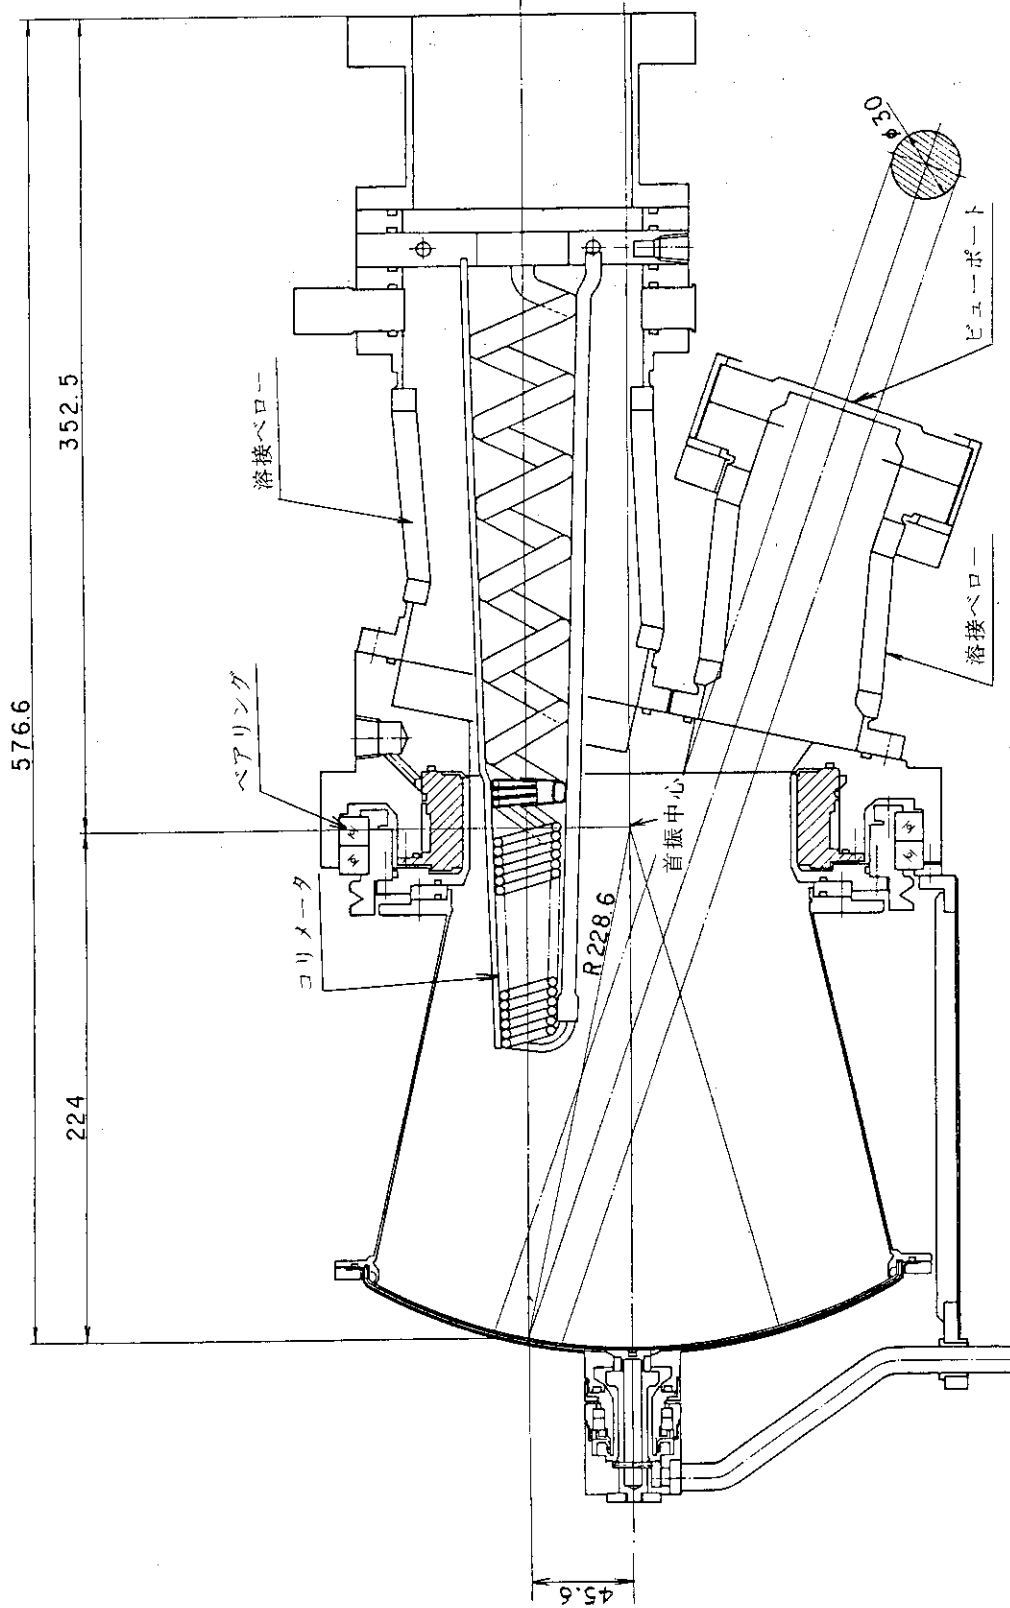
新ジャケット断面構造・ビューポート配置 (平面図)
